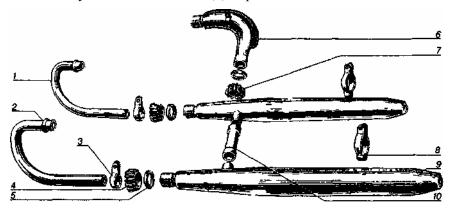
Трубы выпускные с глушителями: I - труба правая; 2 - труба левая; 3 - ушко; 4 - гайка выпускной трубы; 5 - кольцо уплотнительное, 6 - ресивер, 7 - гайка ресивера; 8 - хомут глушителя; 9 - глушитель; 10 - труба соединительная
